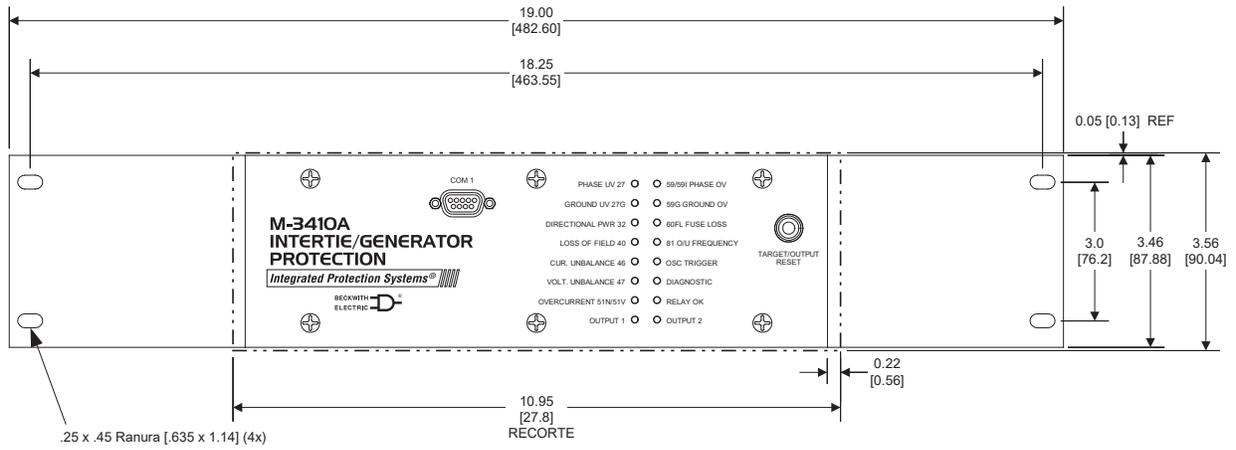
Dimensiones de Montaje del 19" Rack Estándar
